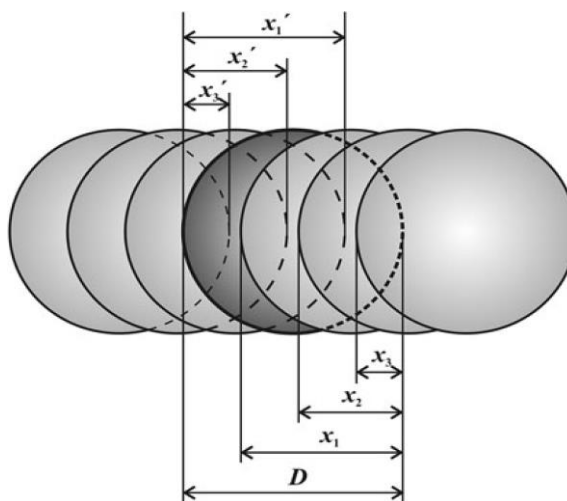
Схема процесса импульсной лазерной сварки
